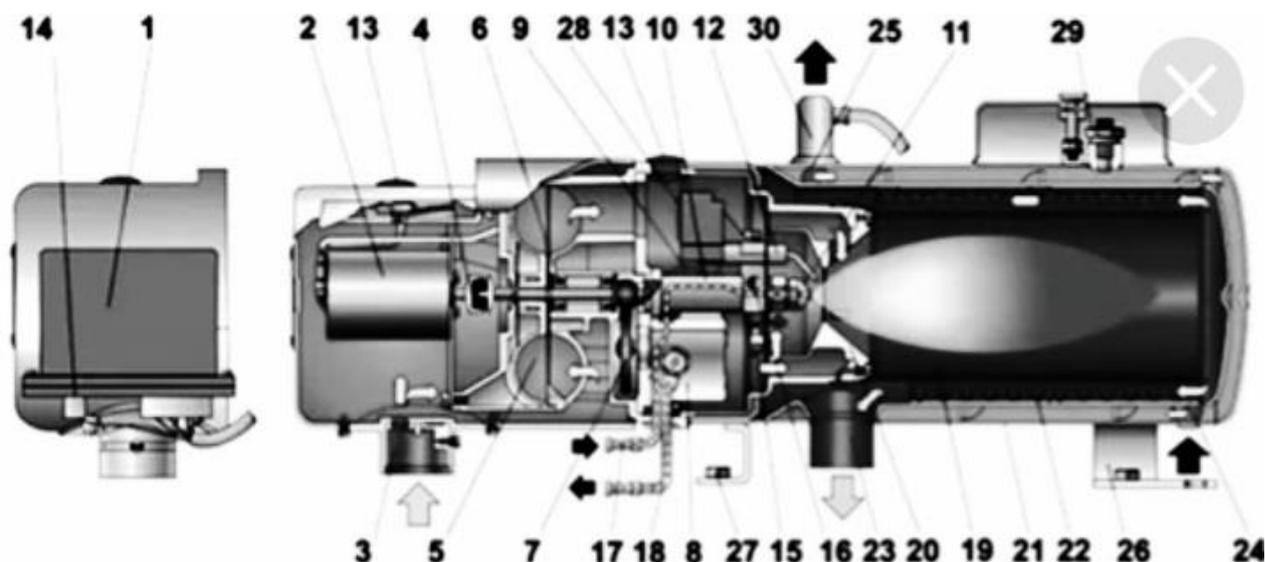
Конструкция автономного жидкостного подогревателя Предпусковой подогреватель: 1 - блок управления; 2 - электродвигатель постоянного тока; 3 - всасывающий патрубок; 4 – муфта; 5 – вентилятор; 6 – подшипник; 7 - зубчатая передача; 8 - топливный насос; 9 - электромагнитный клапан; 10 - корпус форсунки; 11 – форсунка; 12 - электрод зажигания; 13 - держатель электродов; 14 - перепускной клапан; 15 - индикатор пламени; 16 – диск; 17 - трубка подвода топлива; 18 - трубка отвода топлива; 19 – теплообменник; 20 - завихритель; 21, 22 - трубы теплообменника; 23 - патрубок для выхода отработавших тазов; 24 - патрубок «входа»; 25 - патрубок «выхода»; 26,27 - кронштейны подогревателя; 28 - источник питания высоковольтный; 29 - Термопредохранитель; 30, 31 - датчики для управления работой подогревателя.
